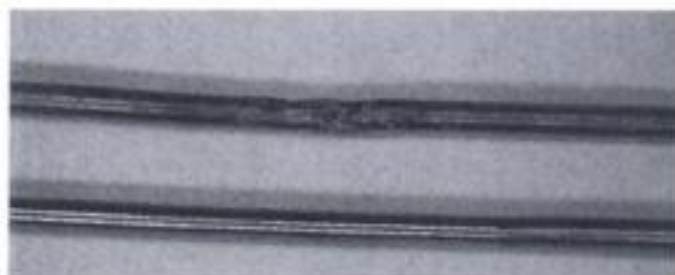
Determinación de la deformación por combado en la soldadura fuerte de una aleación con base de níquel con una soldadura de aleación de base en oro (parte superior), que produjo una zona de difusión de oro-níquel. Si se compara con la barra no-soldada (parte inferior), se aprecia que la barra soldada se ha combado. (Por cortesía de C.E. Ingersoll.)
